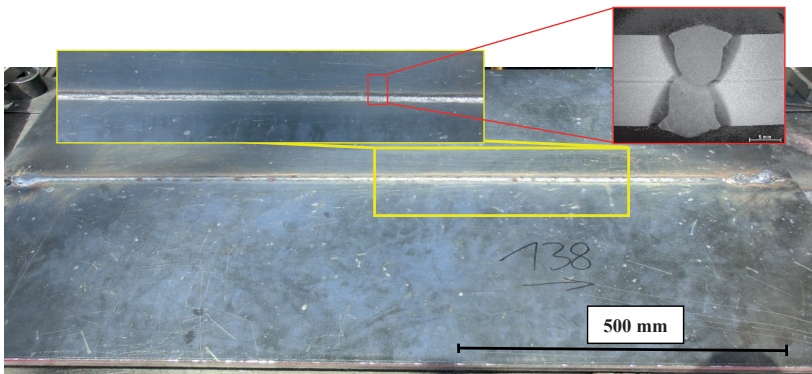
Schweißnaht für die Sichtprüfung
